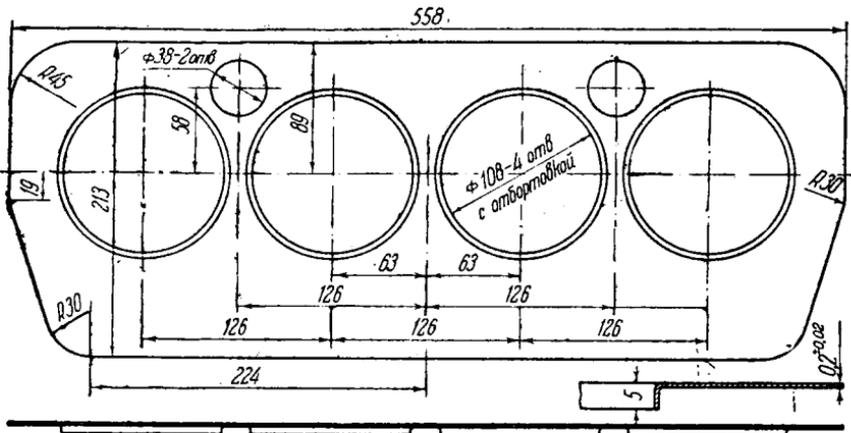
Дет. № 02-02. Лист нижний прокладки головки цилиндров
